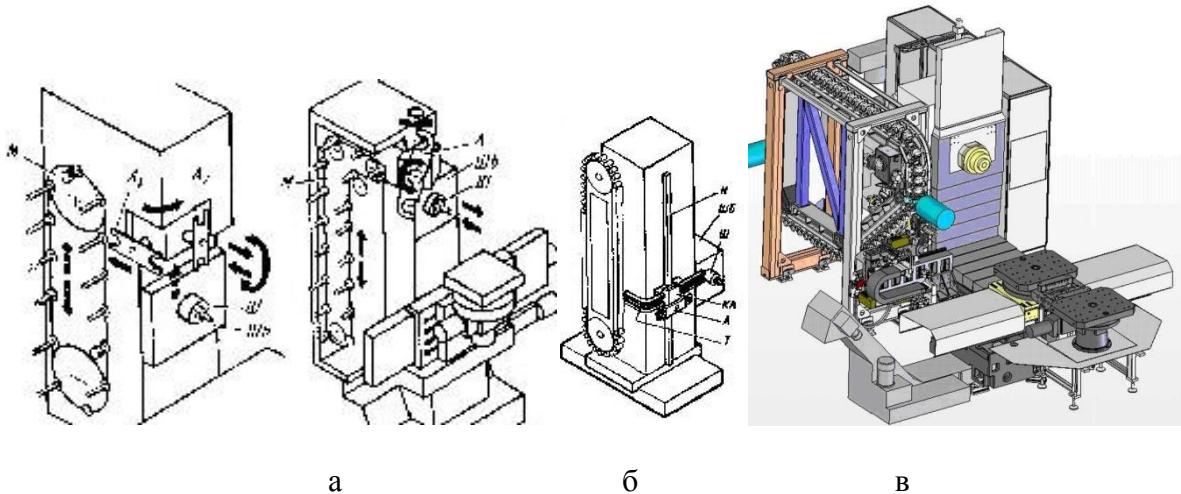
Устройства АСИ при боковом расположении магазина на горизонтальных МС
